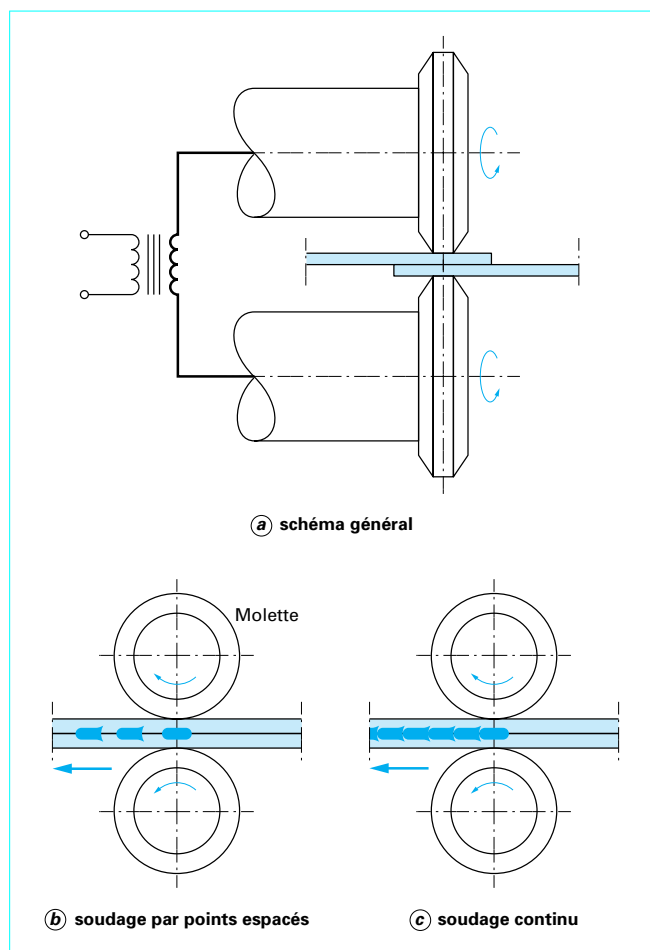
Principe du soudage électrique par résistance à la molette, d'après [17]
